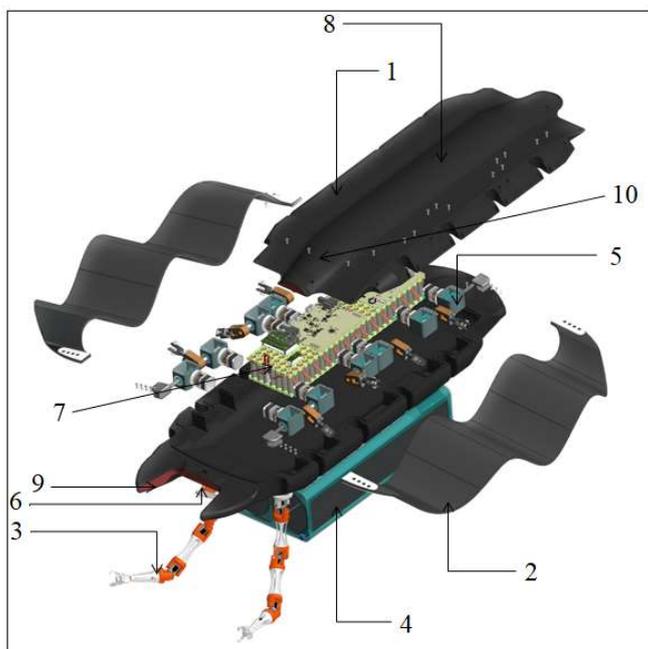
Робот-сборщик: 1 – корпус; 2 – плавники; 3 – руки-манипуляторы для сбора ЖМК; 4 – сборочный отсек; 5 – сервоприводы с редуктором (12 шт); 6 – интеллектуальная камера; 7 – аккумуляторная батарея с блоком электроники; 8 – беспроводная зарядка; 9 – прибор освещения; 10 – гидроакустический приемник системы навигации.
